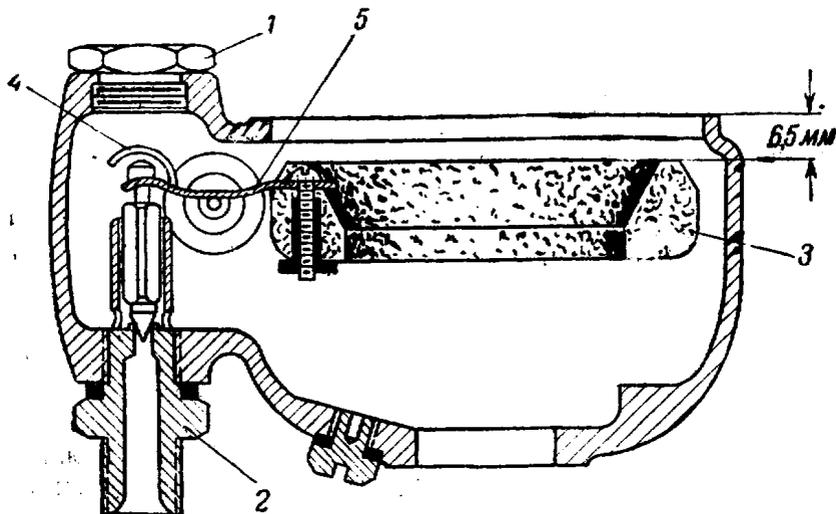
Регулировка уровня топлива в поплавковой камере:
